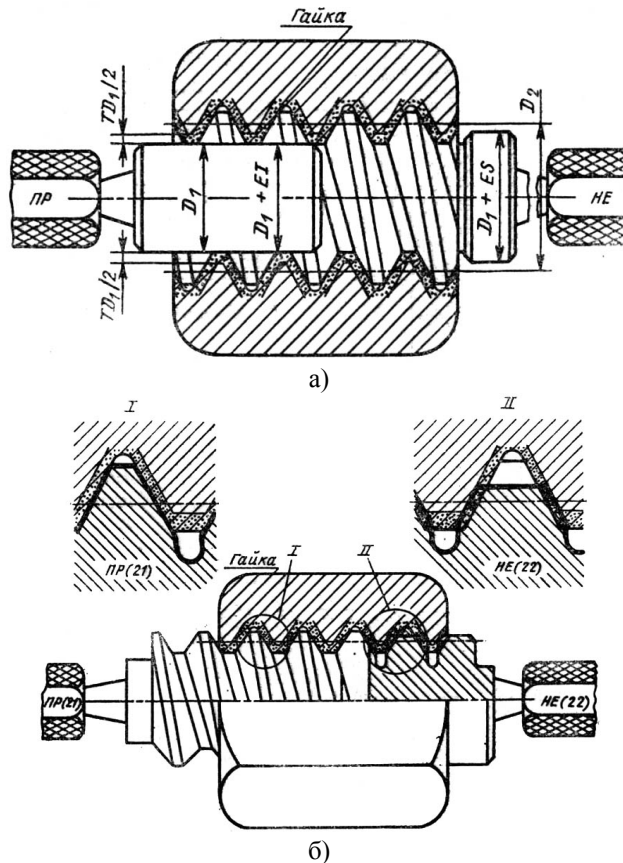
Гладкие калибры-пробки (а) резьбовые калибры-пробки (б) для контроля внутренней резьбы
